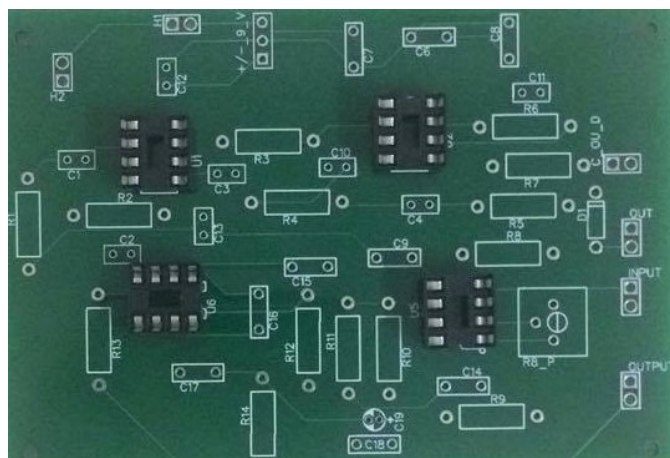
Placa do circuito impresso do protótipo com as bases dos integrados já soldadas.
